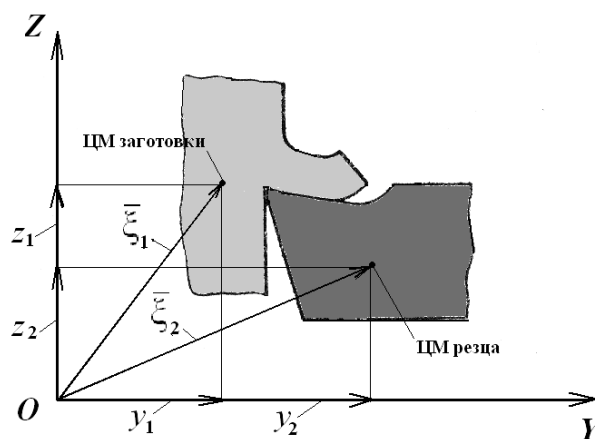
Пример обобщённых координат, с помощью которых описывались колебания заготовки и резца
